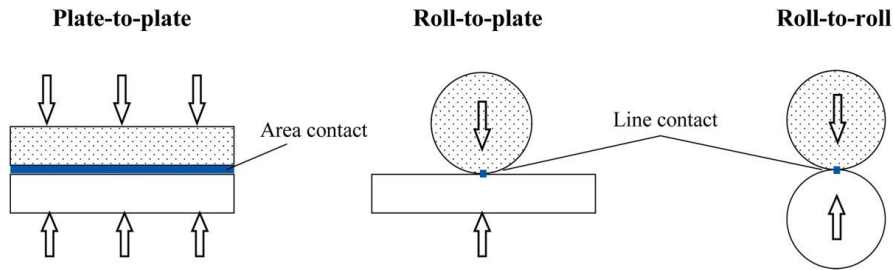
Área o línea de contacto (azul) en la litografía por impresión convencional o en las técnicas de roll to plate o roll to roll[101].
